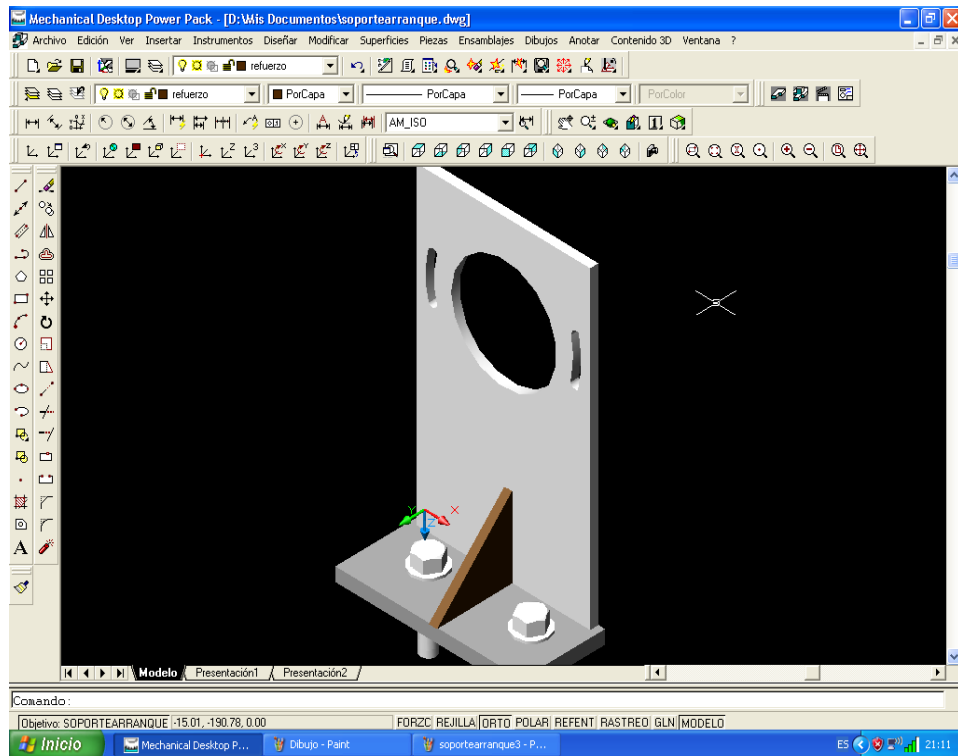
Vista isométrica 2 de la Placa que soporta el motor de arranque
